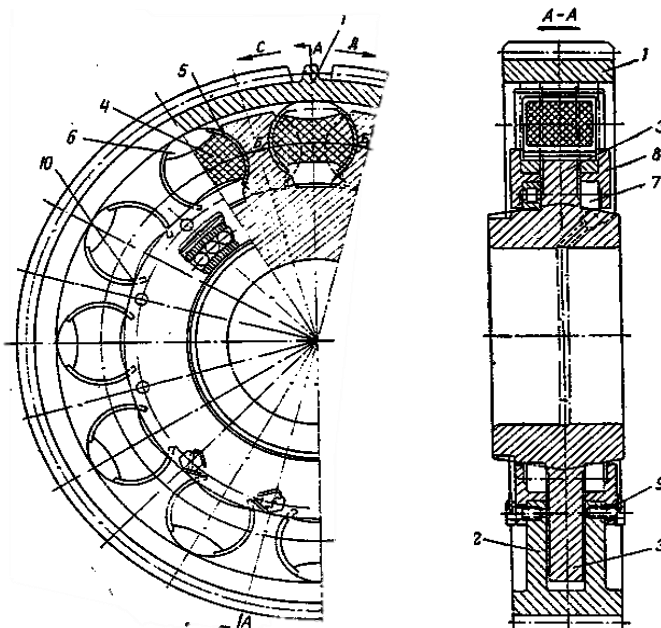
Пружне зубчасте колесо для тягової передачі локомотива
